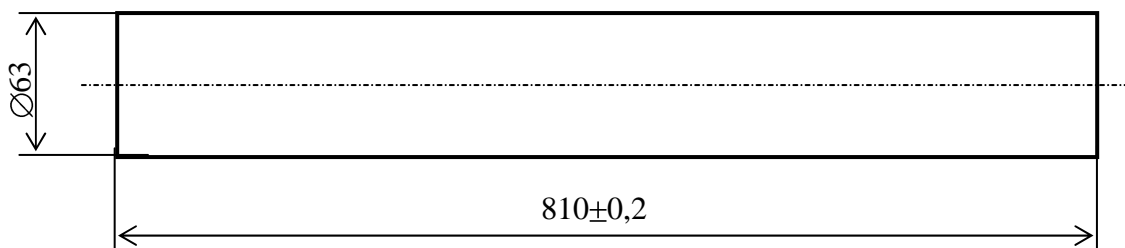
Ескіз заготовки з круглого прокату
